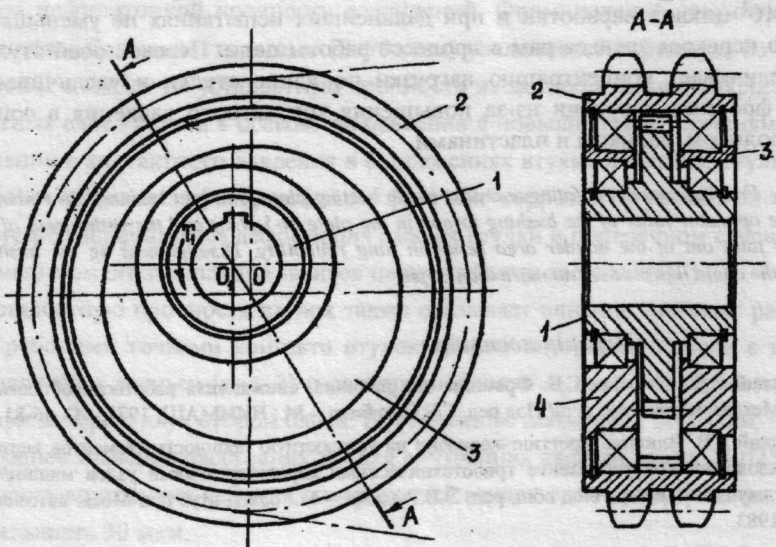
Конструкція зірочки для автоматично регульованої ланцюгової передачі
